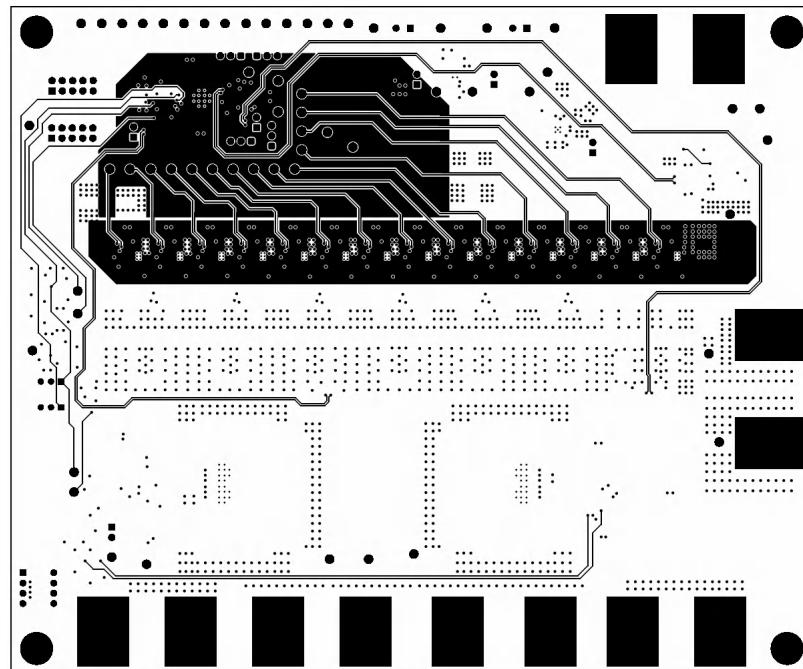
TPS53676EVM-084 PCB 第 3 层 - 信号
